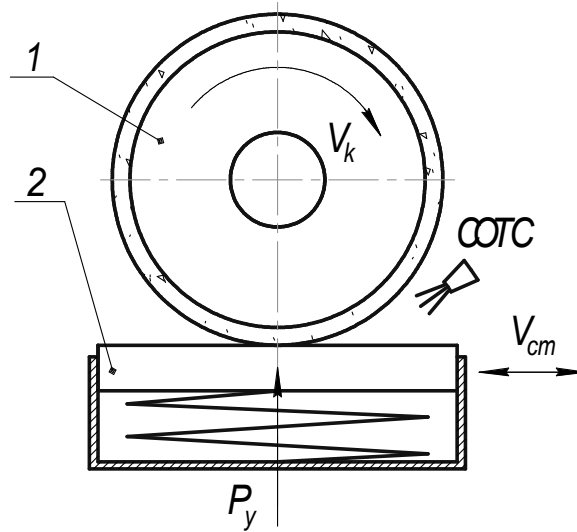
Схема плоского шлифования по упругой схеме периферией круга: 1 – шлифовальный круг, 2 – обрабатываемый образец
